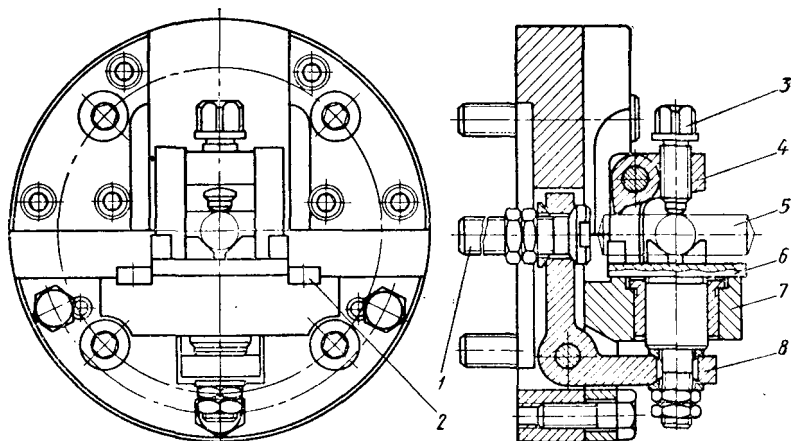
Патрон для подрезки торцов и зацентровки отверстий в деталях типа крестовин и цапф на токарных или револьверных станках
